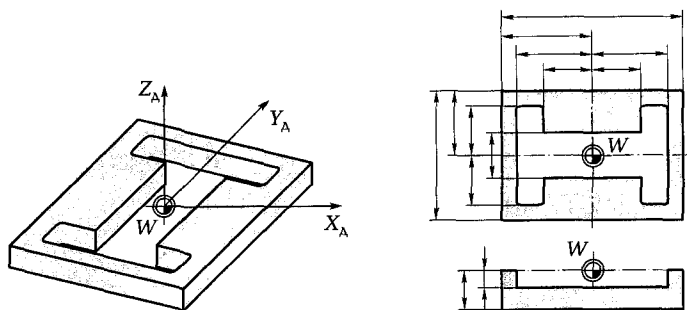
Задание нулевой точки W детали при обработке симметричной детали
